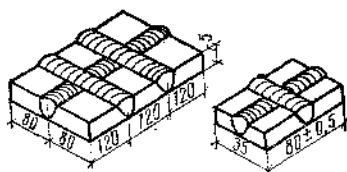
Образцы для испытаний на межкристаллитную коррозию
